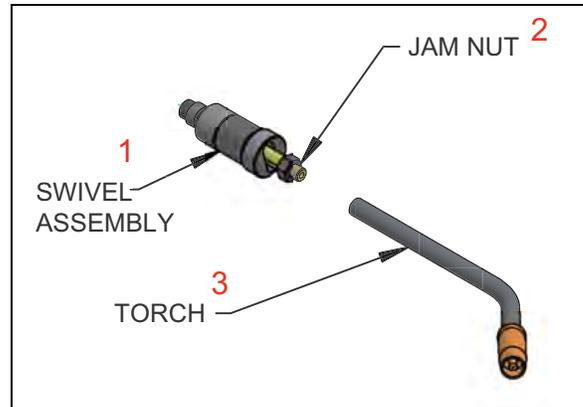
ENSEMBLE PIVOTANT ET TORCHE
